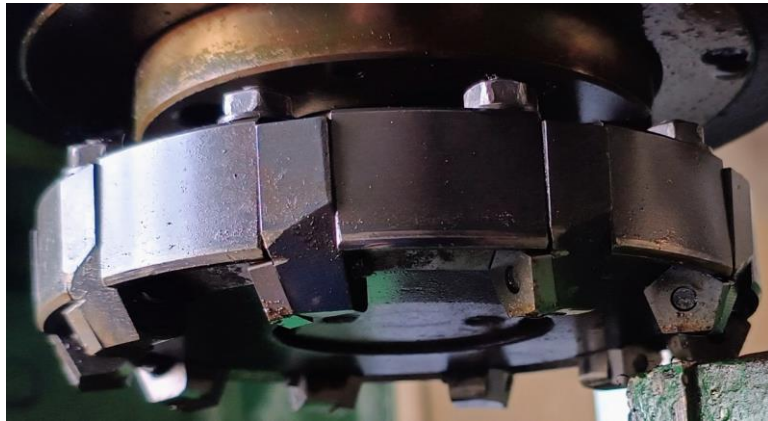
Торцева фреза із змінними твердосплавними п'ятигранними вставками
